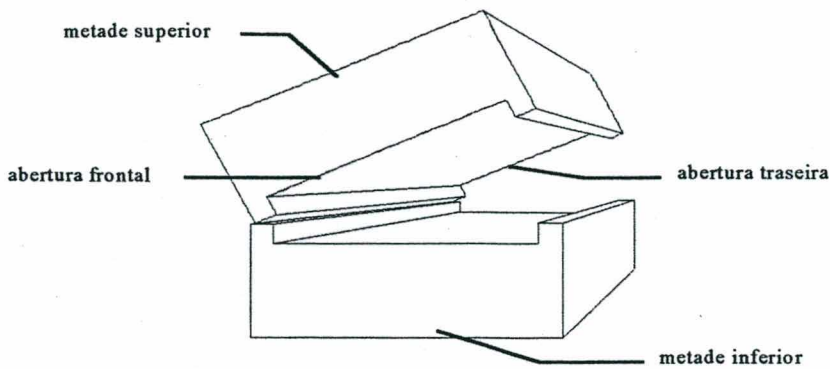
Estrutura metálica do túnel de aquecimento. Caixa metálica bipartida. Representação esquemática.
